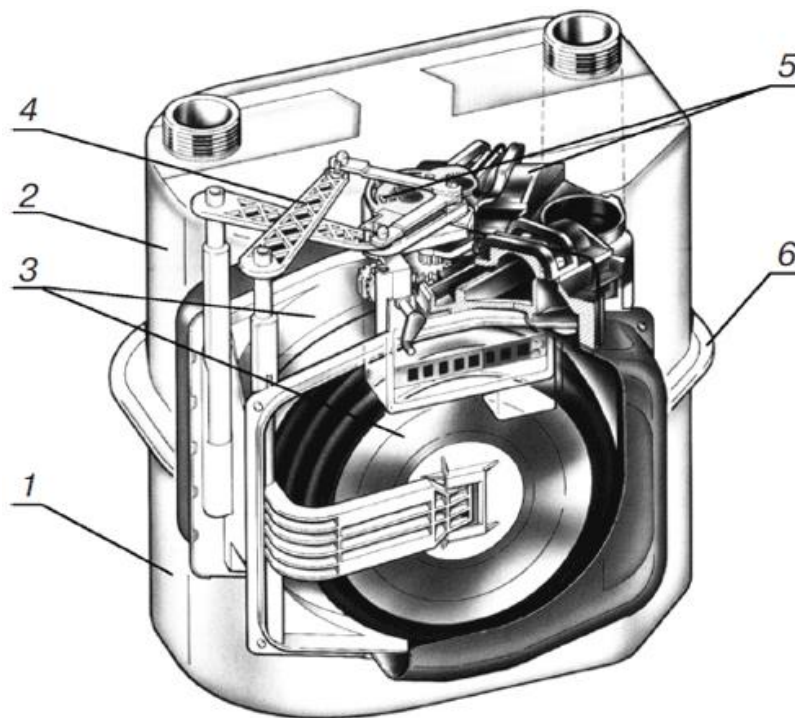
Мембранний лічильник газу: 1 - корпус; 2 - кришка; 3 - вимірювальний механізм; 4 – кривошипно-шатунний механізм; 5 - верхні клапани газорозподільного пристрою; 6 - стяжна смуга
